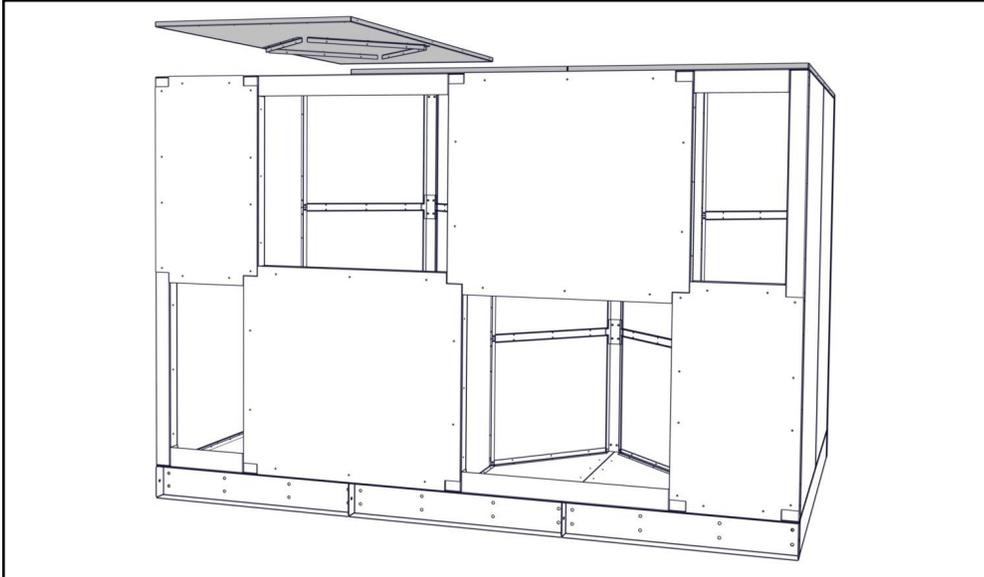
INSTALLER LES ASSEMBLAGES DE TOIT
